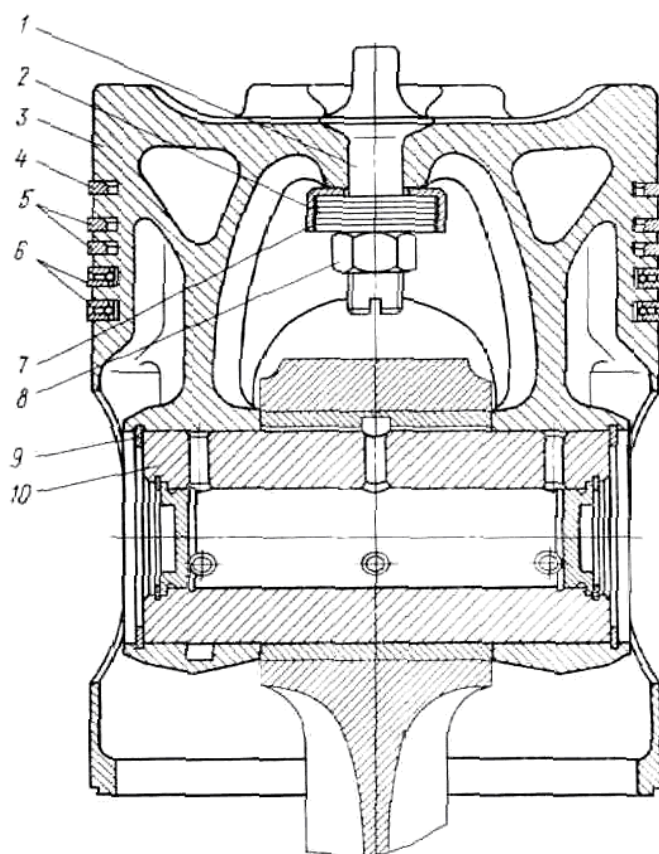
Поршень дизеля РАЧ-185: 1 – коническая насадка; 2 – шайбы; 3 – головка поршня; 4, 5 – компрессионные кольца; 6 – маслосъемные кольца; 7 – втулка; 8 – гайка; 9 – стопорное кольцо; 10 – палец
